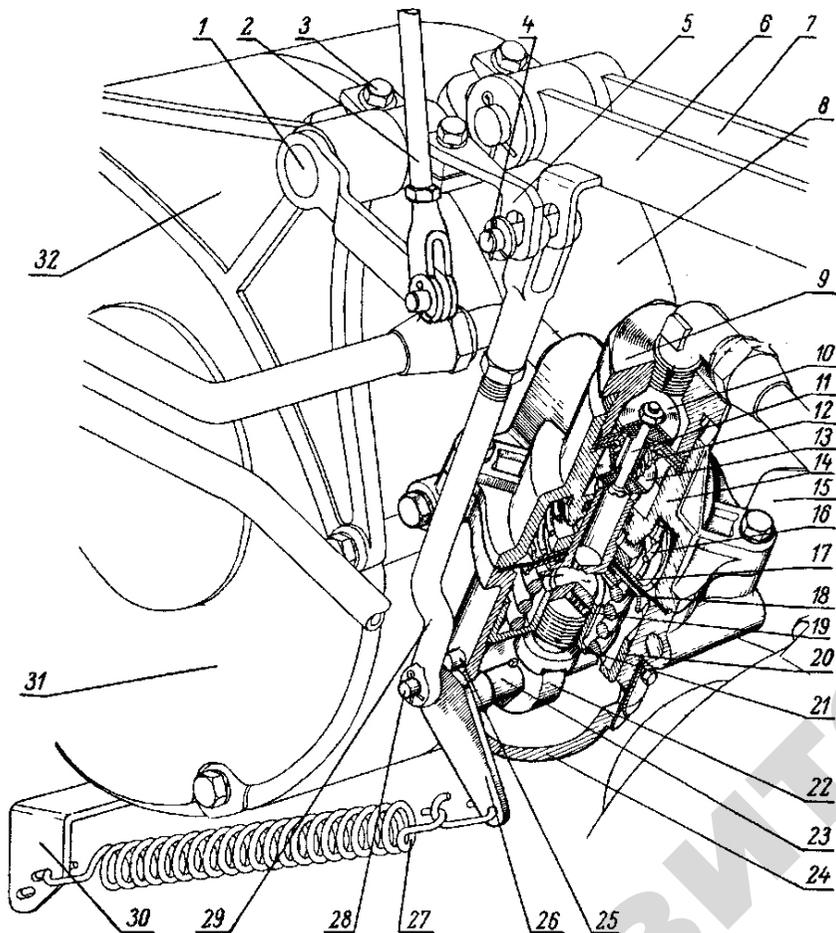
Тормозной кран и его привод (МТЗ-80):
